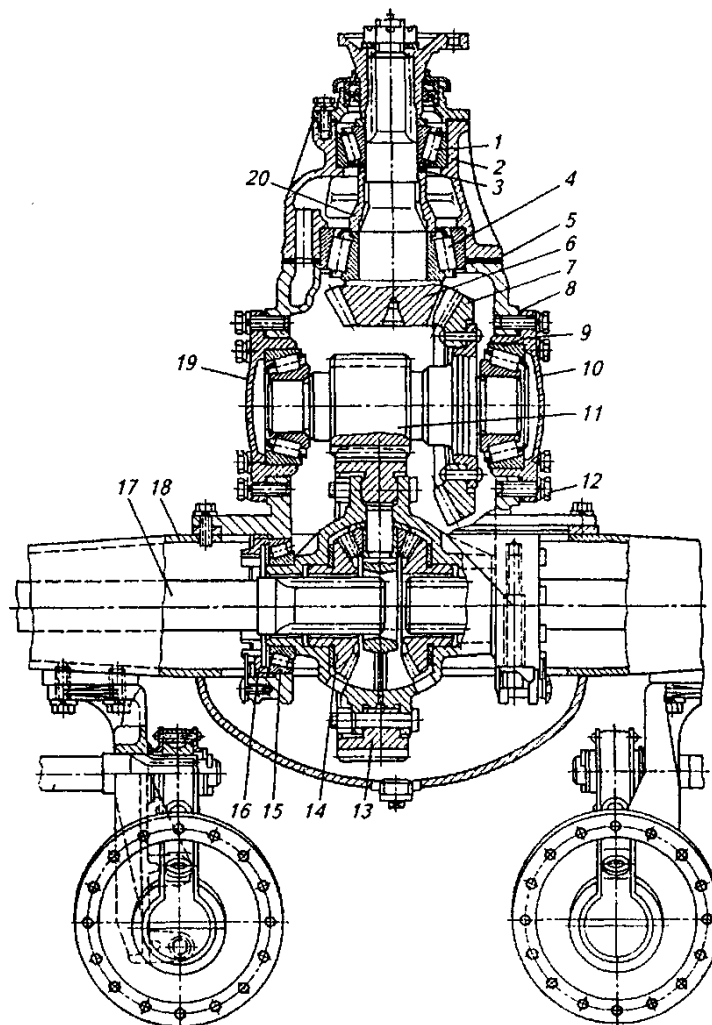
Двойная главная передача автомобиля ЗИЛ-431410: 1 — передний конический подшипник вала конической шестерни; 2 — стакан подшипника вала конической шестерни; 3 — регулировочные шайбы; 4 — задний конический роликоподшипник; 5 — прокладка для регулировки зацепления конических зубчатых колес; 6 — коническая шестерня; 7 — коническое зубчатое колесо; 8 — регулировочные прокладки; 9 — конические роликоподшипники цилиндрической шестерни; 10, 19 — крышки соответственно правого и левого подшипников; 11 — цилиндрическая шестерня; 12 — картер главной передачи; 13 — цилиндрическое зубчатое колесо; 14 — полуосевая шестерня; 15 — роликоподшипник дифференциала; 16 — регулировочная гайка подшипника дифференциала; 17 — полуось; 18 — картер моста; 20 — распорная втулка
